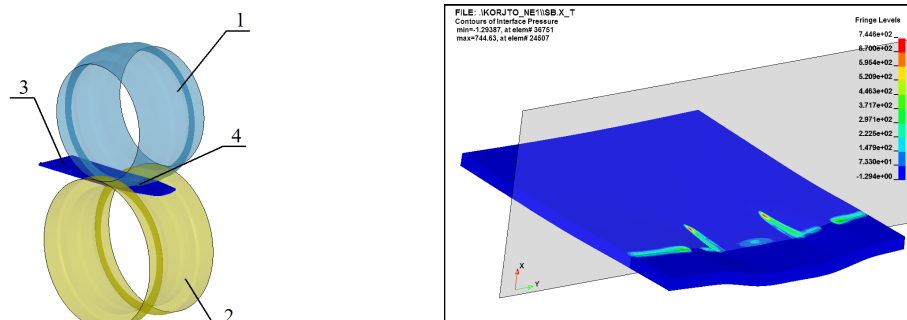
Моделирование 1 перехода: слева – общий калибр с заготовкой, справа – общий вид заготовки и контакта; 1 – верхний ролик, 2 – нижний ролик, 3 – заготовка, 4 – зоны контакта
